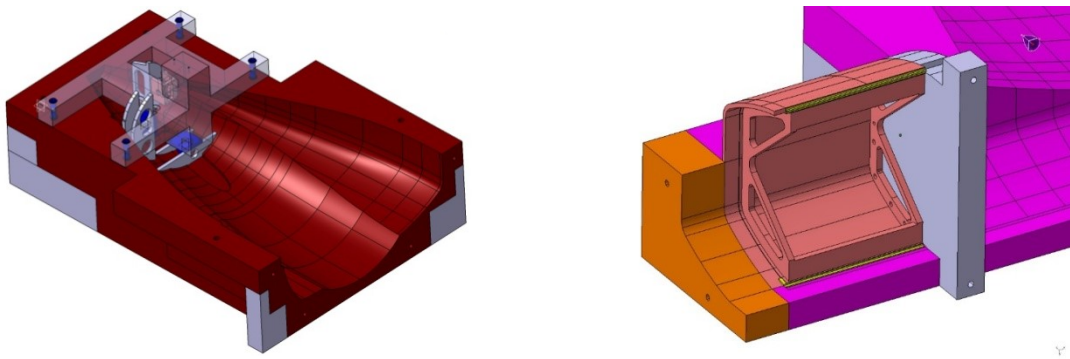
Hilfslehren zum Positionieren der Einbauten in die Laminatkonstruktion
